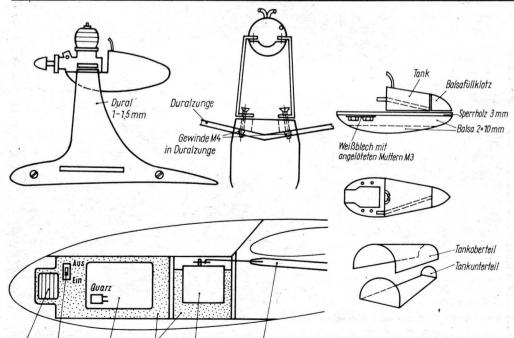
Befestigung des Motorteils am Rumpf. Die abgewinkelten Konsolen werden zwischen Motorflansch und Motorträger geschraubt. Links: Träger über die Zungen am Rumpf geschoben. Rechts: Träger auf die Rumpfoberseite geschraubt. Die Schraubstellen werden von der Zunge bis zur Rumpfoberseite mit Kiefer ausgefüllt
